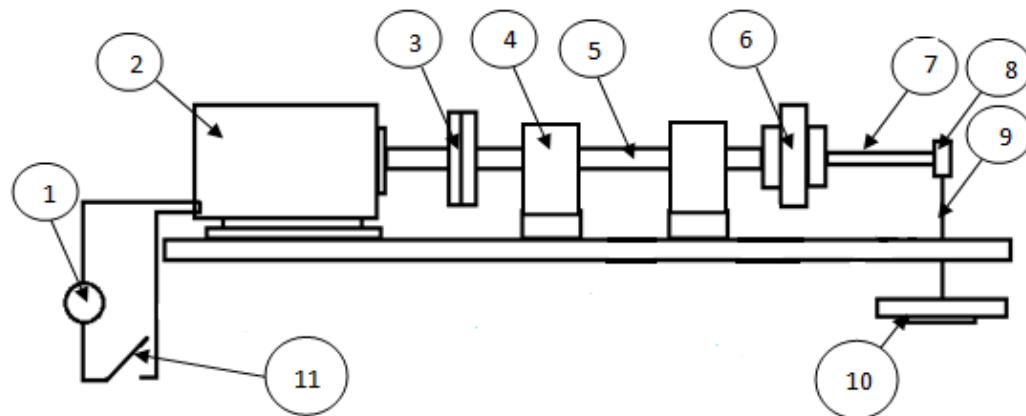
Skema Instalasi Mesin Bubut untuk Pengelasan Gesek
